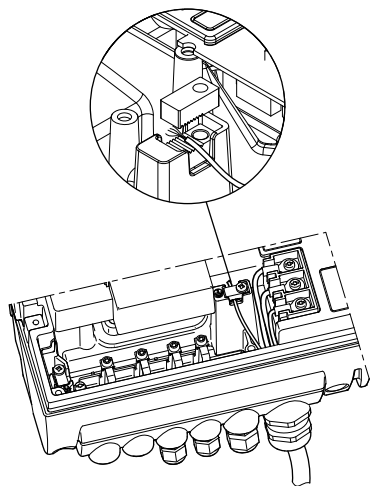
Соединение отдельным защитным проводом с использованием одного проводника 4-жильного силового кабеля (с поперечным-сечением минимум 10 мм²)
